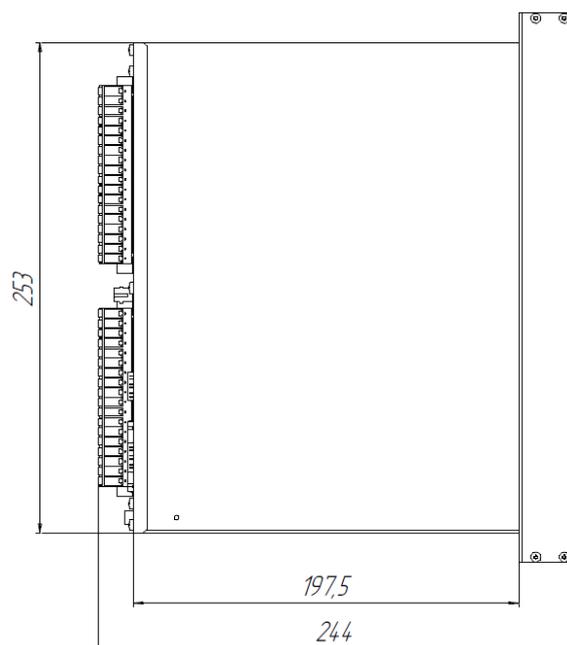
Габаритные и установочные размеры терминала БЭ2704 096/097 (вид сбоку)
